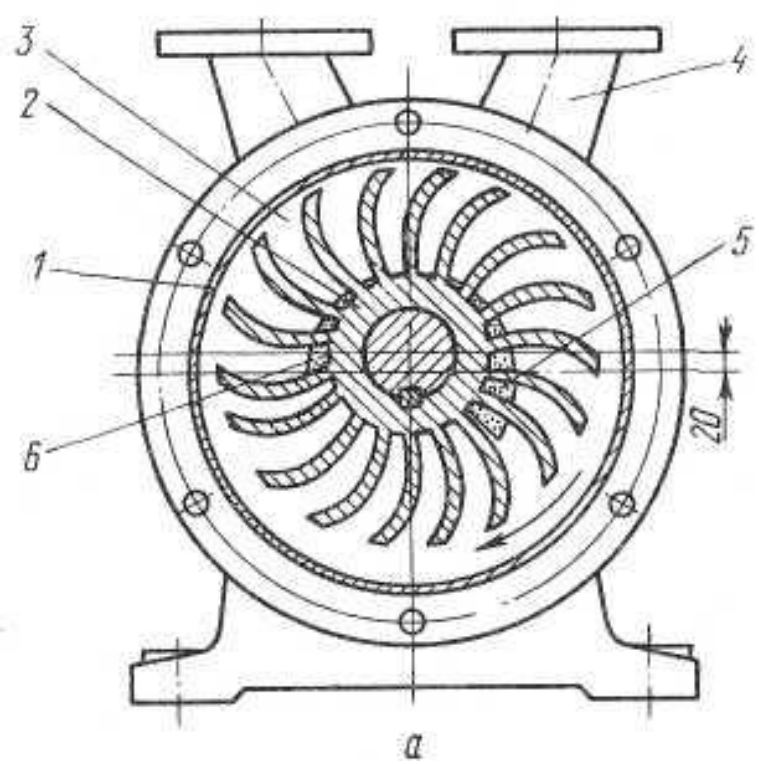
Воздуходувка марки ТВ-80-1,6:
